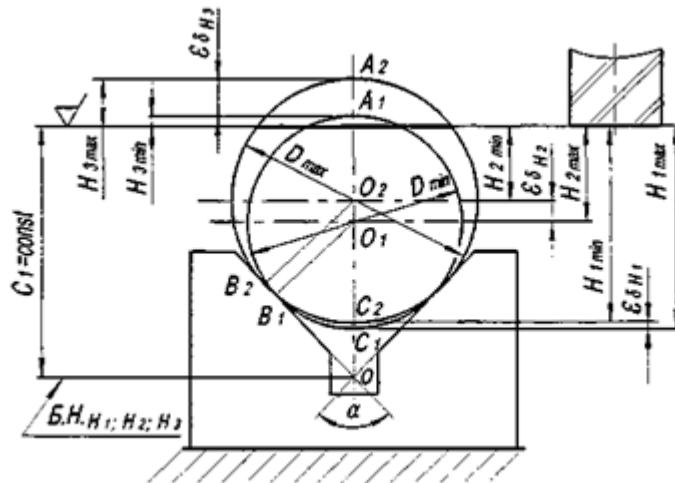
Схема установки деталі типу «вал» на призму
